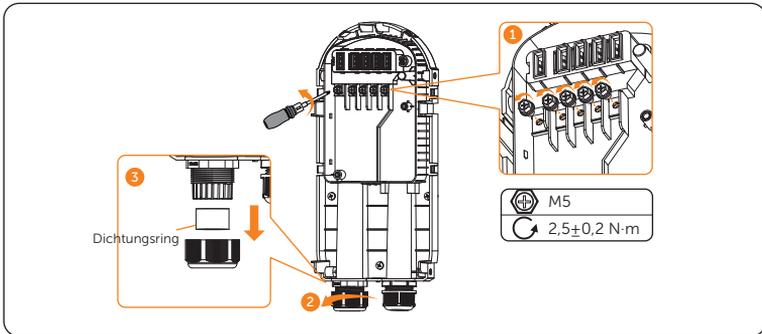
Die Schrauben entfernen und die Überwurfmutter lösen
